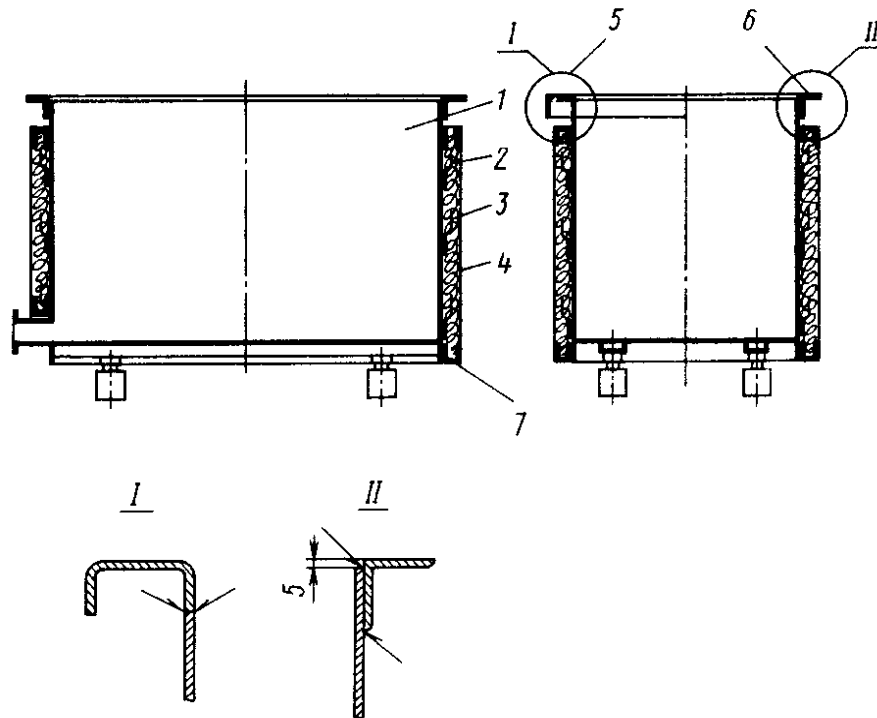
Корпус ванны с теплоизолированными стенками: 1 – корпус ванны; 2 – минеральная вата; 3 – устройство для крепления теплоизоляции; 4 – лист; 5 - обвязка бортов из гнутых швеллеров; 6 – обвязка бортов из уголков; 7 – рама
